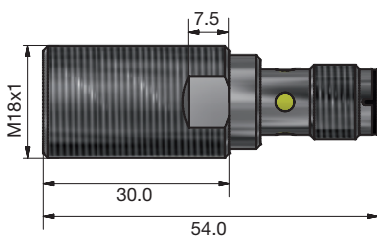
Kurze Ausführung, bündiger Einbau, Steckversion
